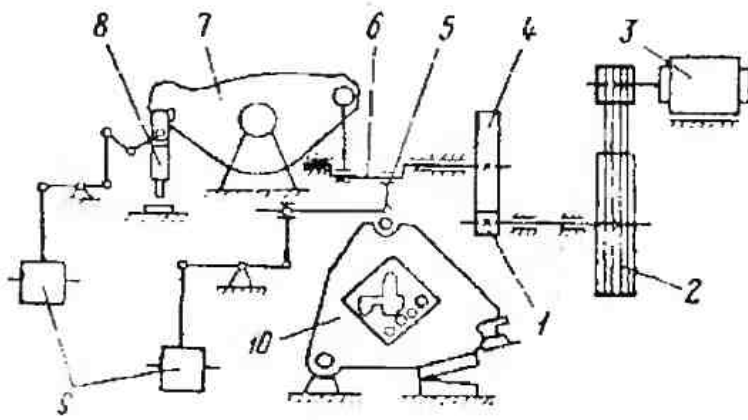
Схема кинематическая: 1 – вал-шестерня; 2 – маховик; 3 – электродвигатель; 4 – колесо зубчатое; 5 – шатун; 6 – вал; 7 – баланси́р; 8 – ползун прессы; 9 – электромагнит; 10 – ползун сортополосовой секции.
